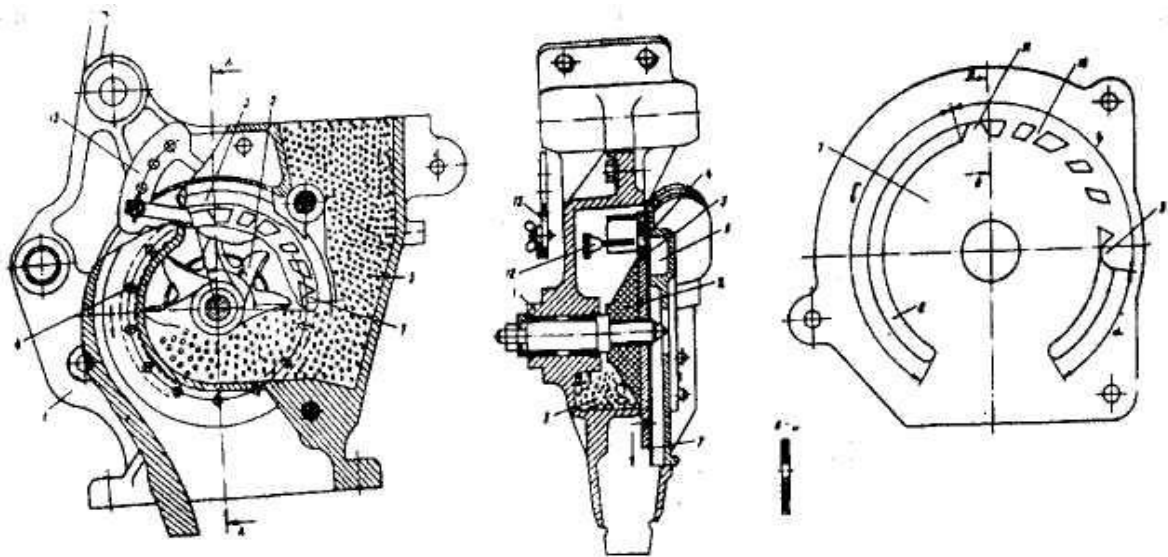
Висівний апарат з комбінованою прокладкою: 1 - корпус; 2 - ворушилка; 3 - висівний диск; 4 - наскрізні отвори диска; 5 - насіннева камера; 6 - вакуумна камера; 7 - капронова комбінована прокладка; 8 - кільцевий виріз; 9, 10, 11 - перемички; 12 - відбивач; 13 - регулятор відбивача
